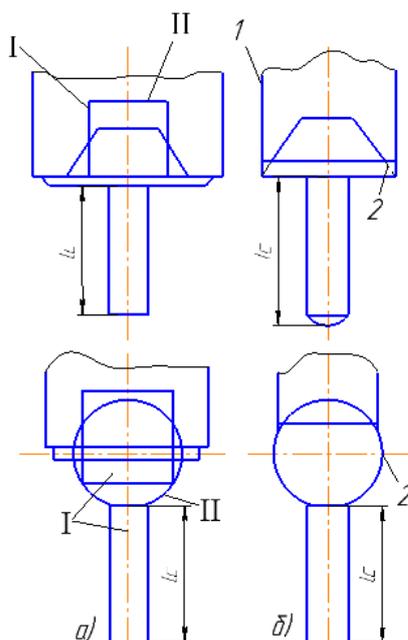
Поковки с конической и шаровидной головками, получаемые в штампах: а — открытым; б — закрытым; 1 — контур пуансона; 2 — напуск; I, II — переходы; l_c — длина стержня
